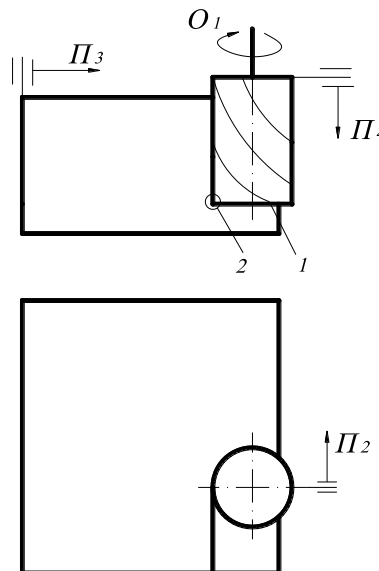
Схема фрезерування уступа кінцевою фрезою
